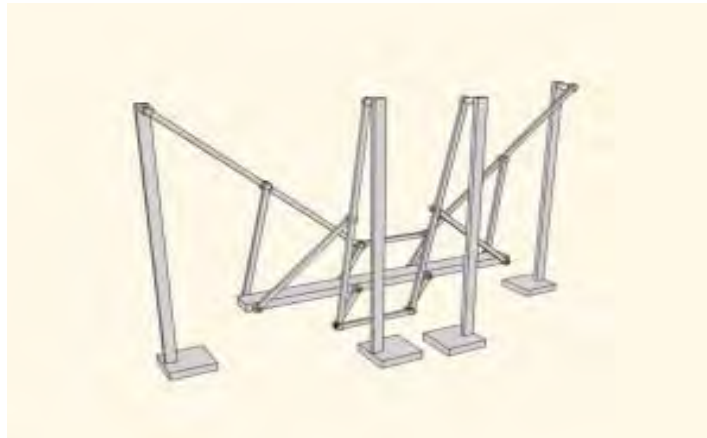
Esta máquina fue un éxito de la Exposición Universal de París en 1878 [34]
